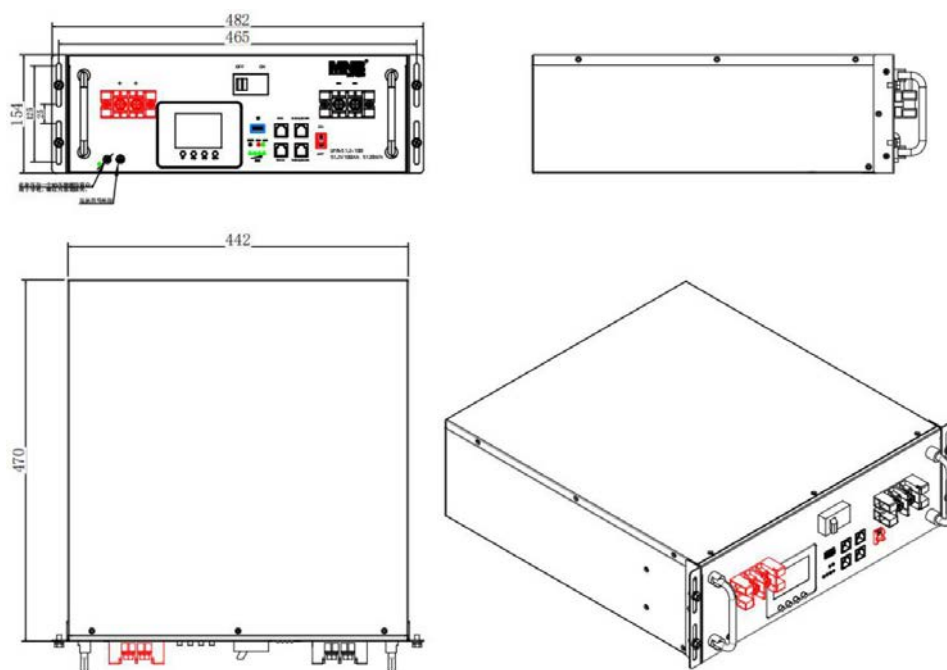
Внешний вид и габаритные размеры LPR-51.2-100 PRO
